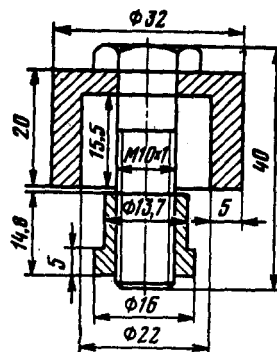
Съёмник для выпрессовки седла впускного клапана компрессора
